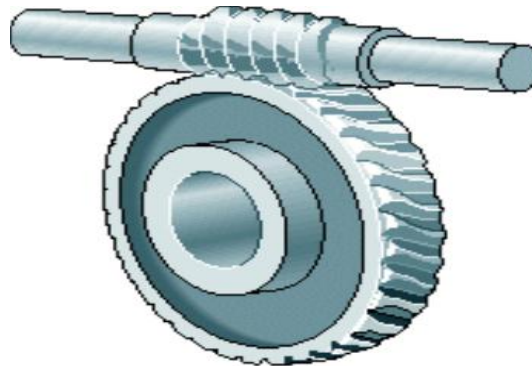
Engranaje de transmisión por tornillo sin fin.
